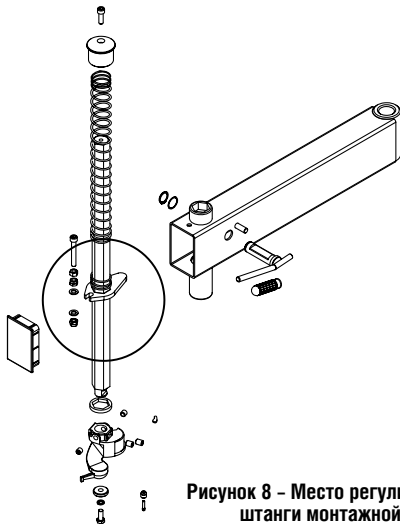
Место регулировки зажима штанги монтажной головки
